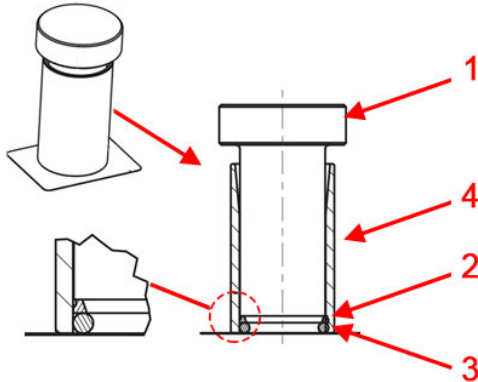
O-Ring im Montagewerkzeug positionieren
